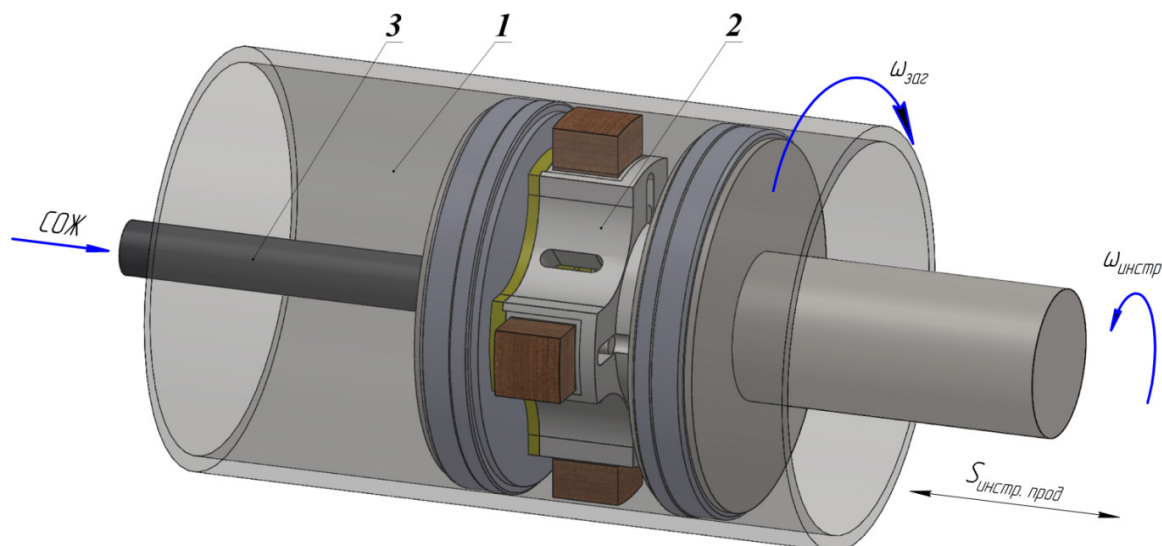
Схема шлифования отверстия соосным инструментом с радиально-подвижными абразивными брусками (1 – заготовка; 2 – соосный инструмент с торцовыми уплотнениями; 3 – трубопровод для подвода СОЖ).
